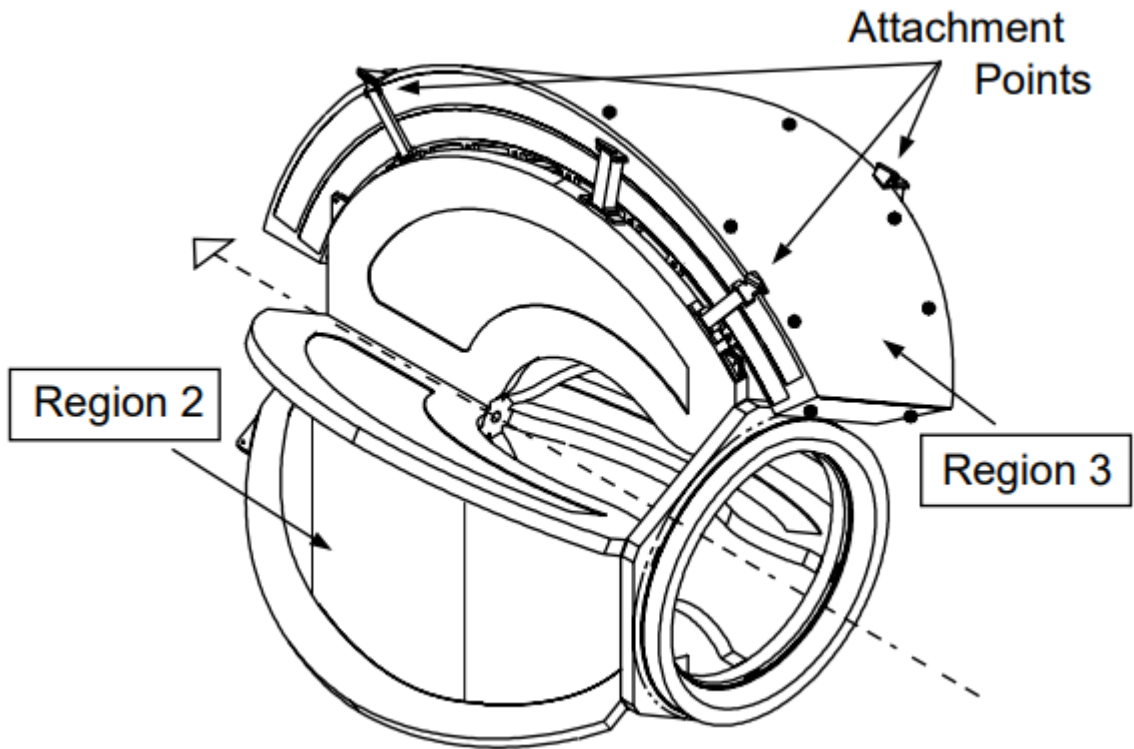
Схематическое устройство дрейфовой камеры.
